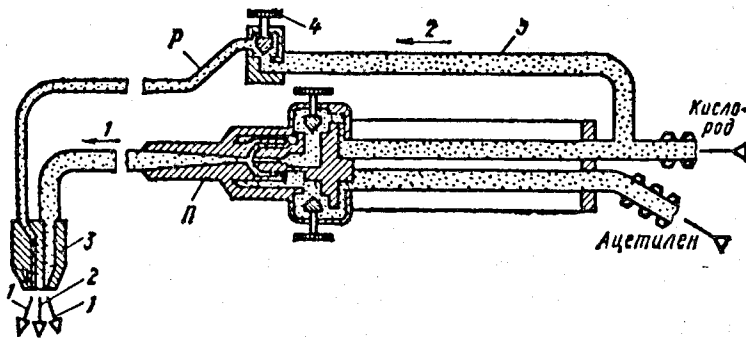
Схема газокислородного резака: Р — режущая часть; П — подогревающая часть
